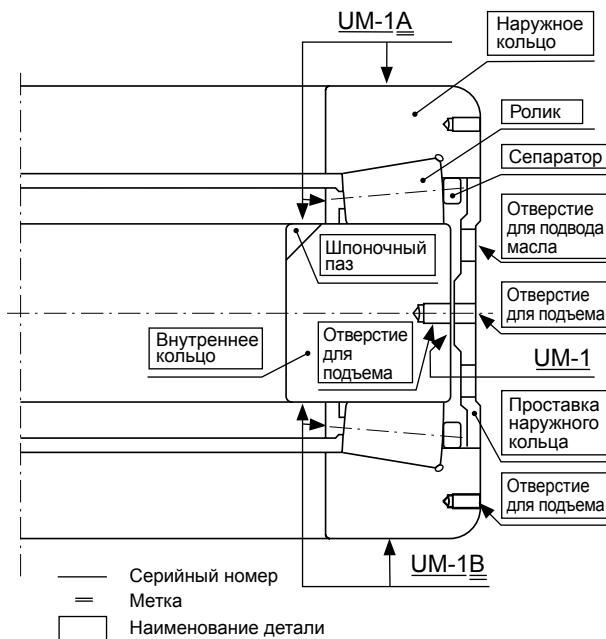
Наименование деталей и примеры маркировки (двухсторонний конический упорный роликоподшипник)
